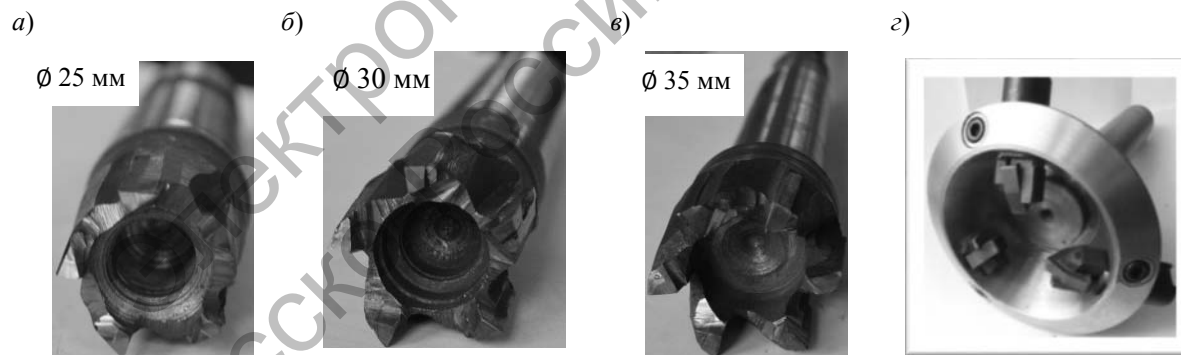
Фрезы для обработки сферических поверхностей деталей: а, б, в – концевые напайные фрезы; г – сборная фреза
